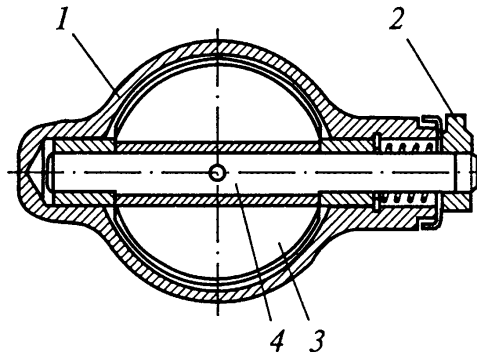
Моторний гальмівний механізм: 1 – корпус; 2 – важіль; 3 – заслінка; 4 – вал
